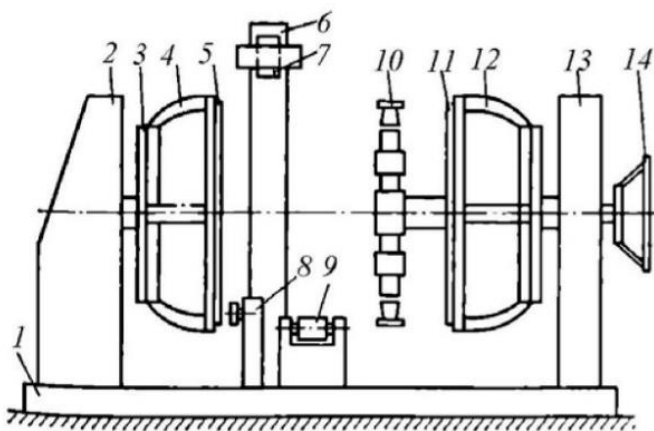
Схема двухопорной установки для сварки кольцевых швов
